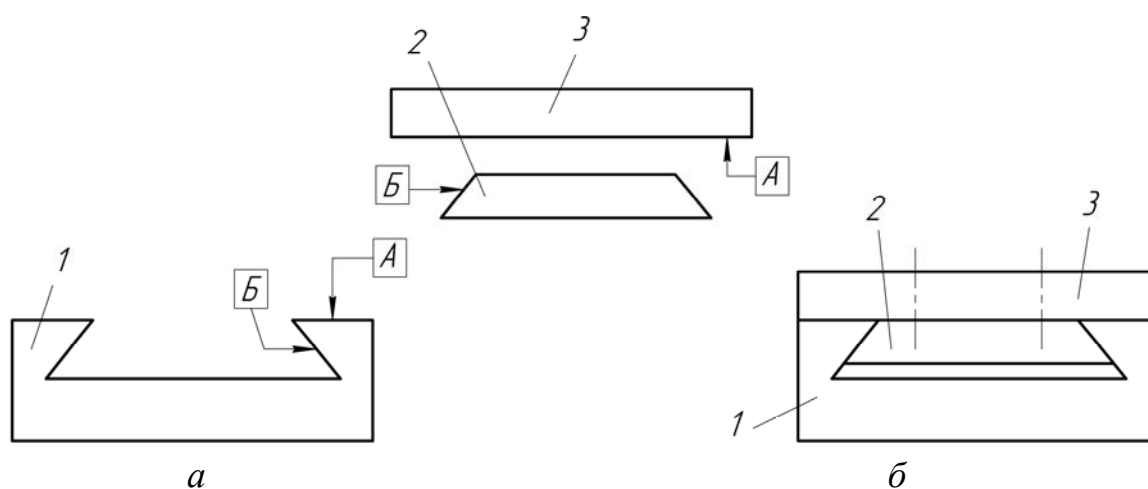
Сборка узла с направляющей типа «ласточкин хвост»
